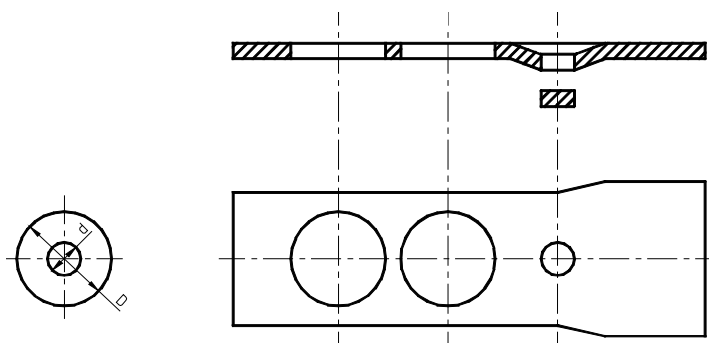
Схема штамповки заготовок тарельчатых пружин с использованием штампа последовательного действия
